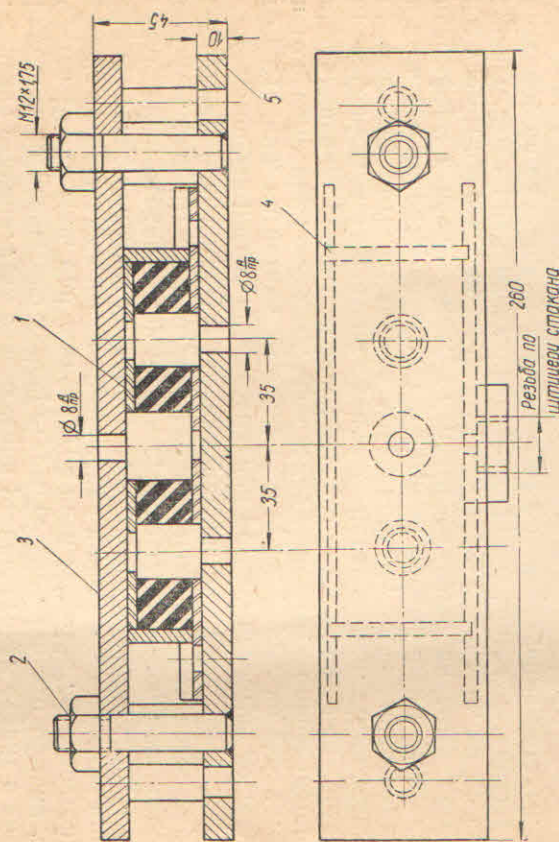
Пресс-форма в сборе с деталью № 20—1001044 — подушка задней опоры двигателя нижняя в сборе:
